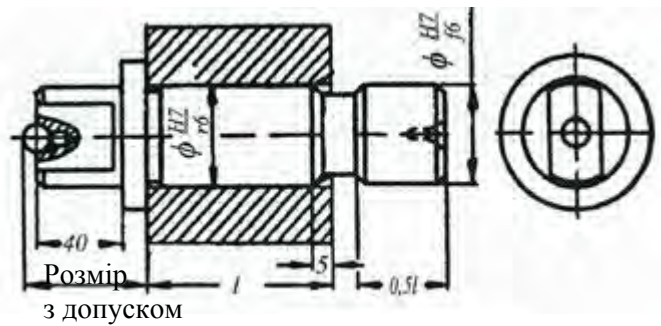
Установка заготовок на жорсткій оправці (посадка з натягом)
